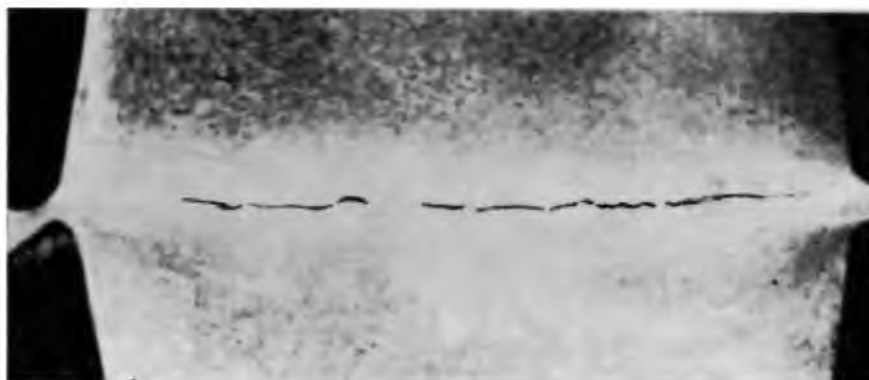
Закалочная трещина в штамповке из сплава АК8
